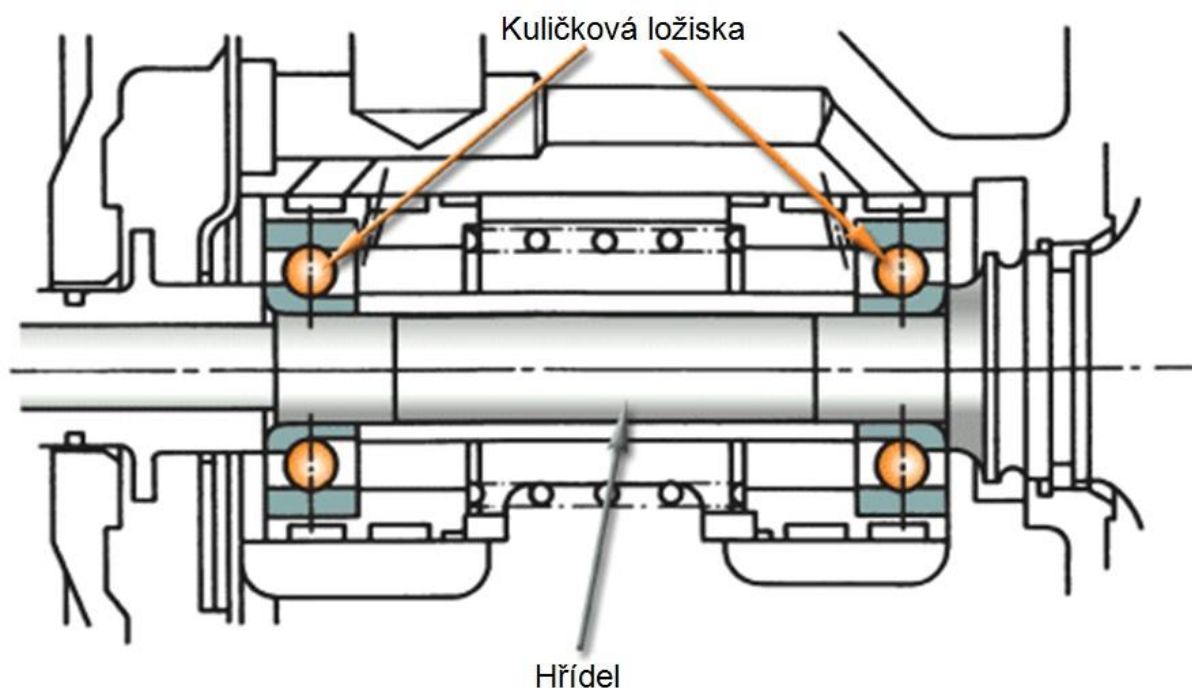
Soustava rotoru a axiální součástky [1]
